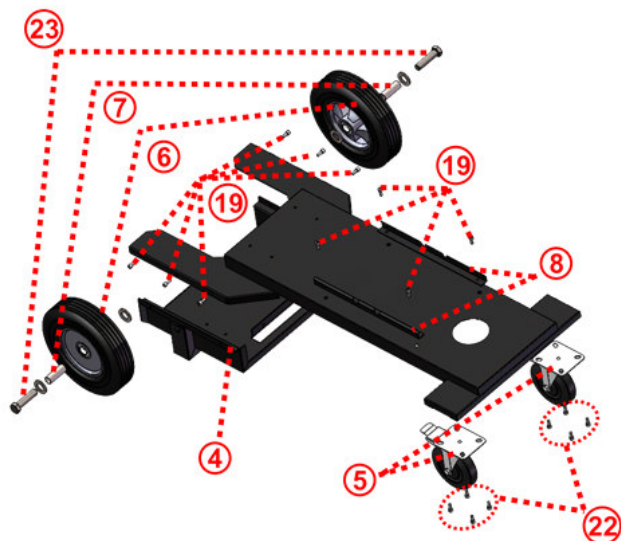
Montage des Schweißgerätwagens Schritt 1
